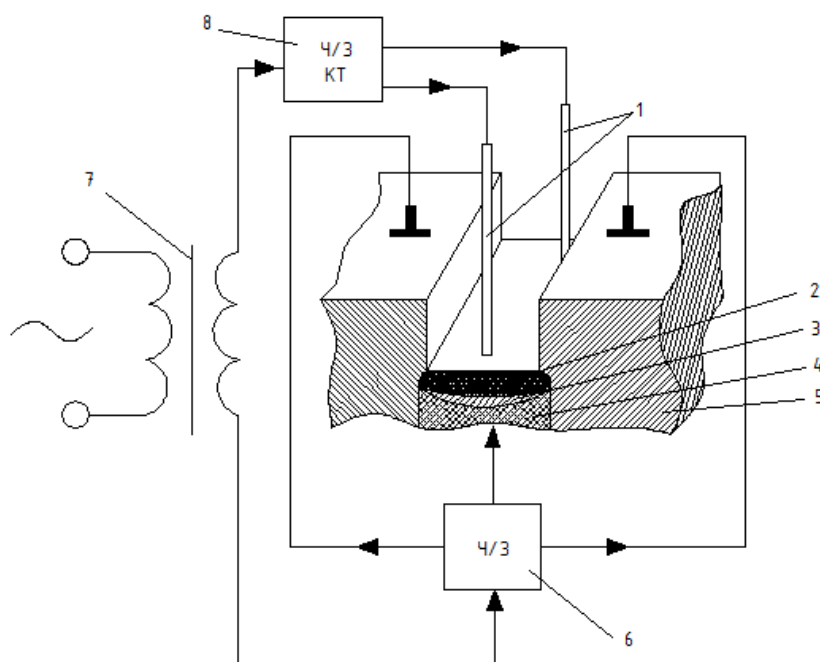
Схема скоростной ЭШС [24]: 1 – электроды; 2- шлаковая ванна; 3- металлическая ванна; 4- сварочный шок; 5- изделия; 6- трехканальный преобразователь тока; 7 – источник питания; 8- двухканальный коммутатор тока.
